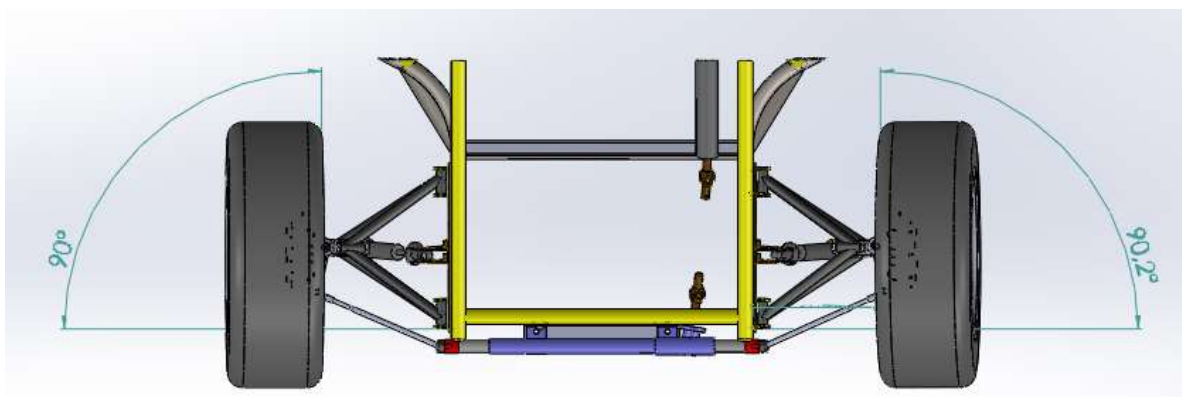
Efeito Bump Steering direcção paralela (vista superior)
